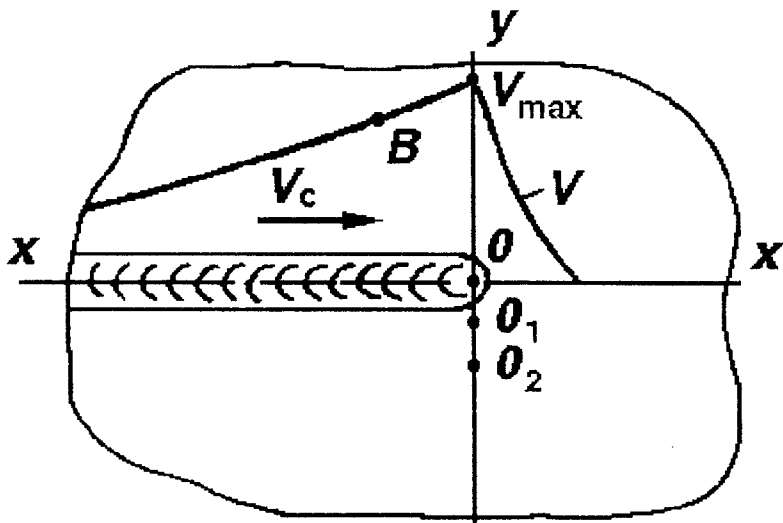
Схема перемещения одной из свариваемых кромок пластины при сварке в направлении OY .
